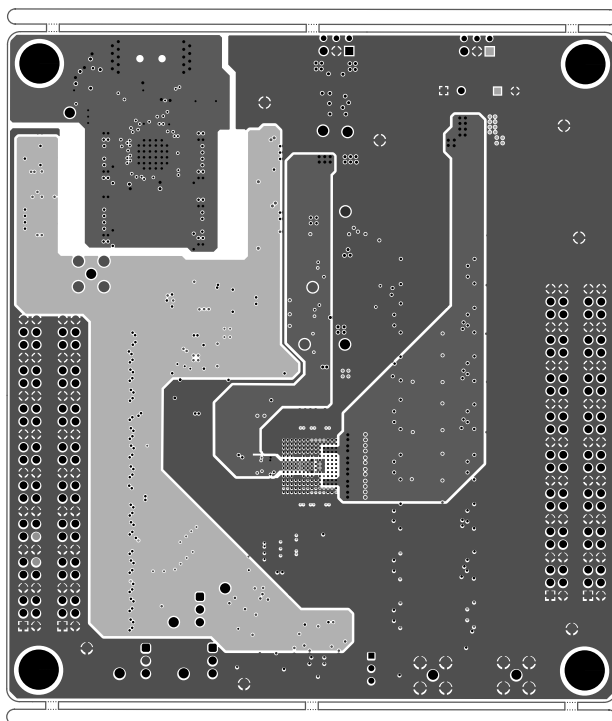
PCB 第 9 层 (接地 5/电源 2)
